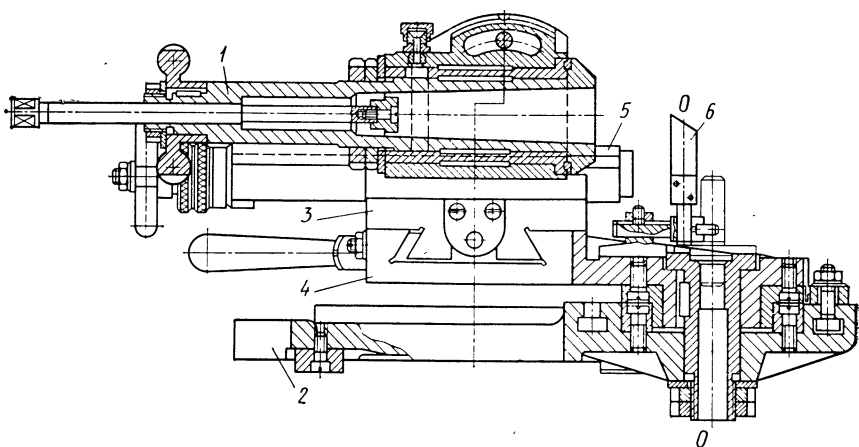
Приспособление для заточки зенкеров по радиусу.
